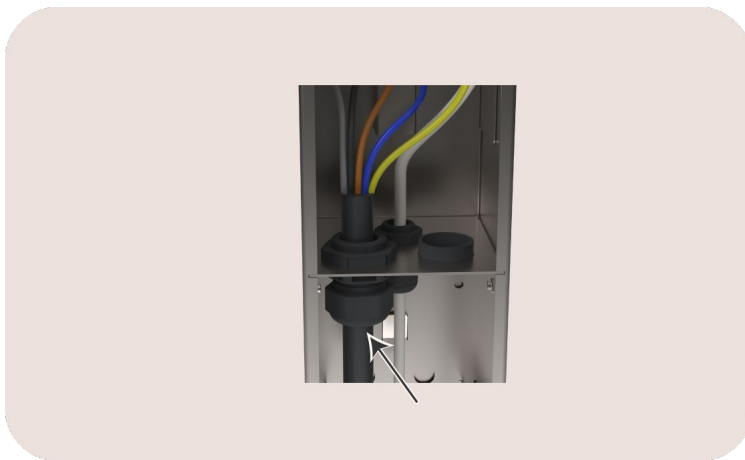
Ansicht der Löcher für die Kabeleinführung
